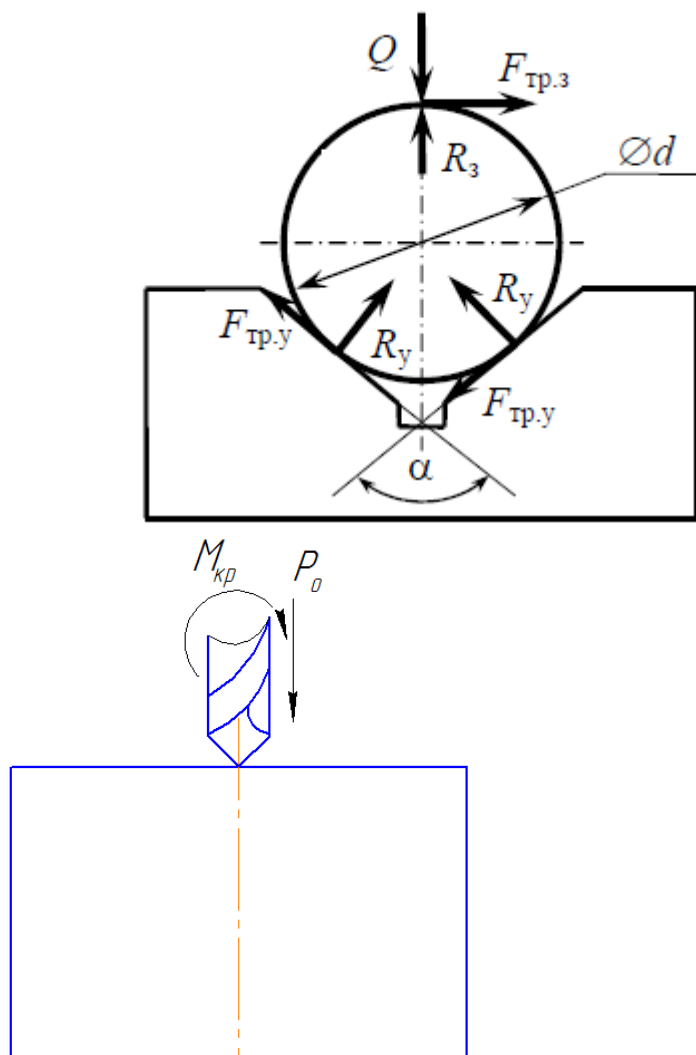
Схема закріплення заготовки з постановкою всіх сил, що діють на неї в процесі обробки
